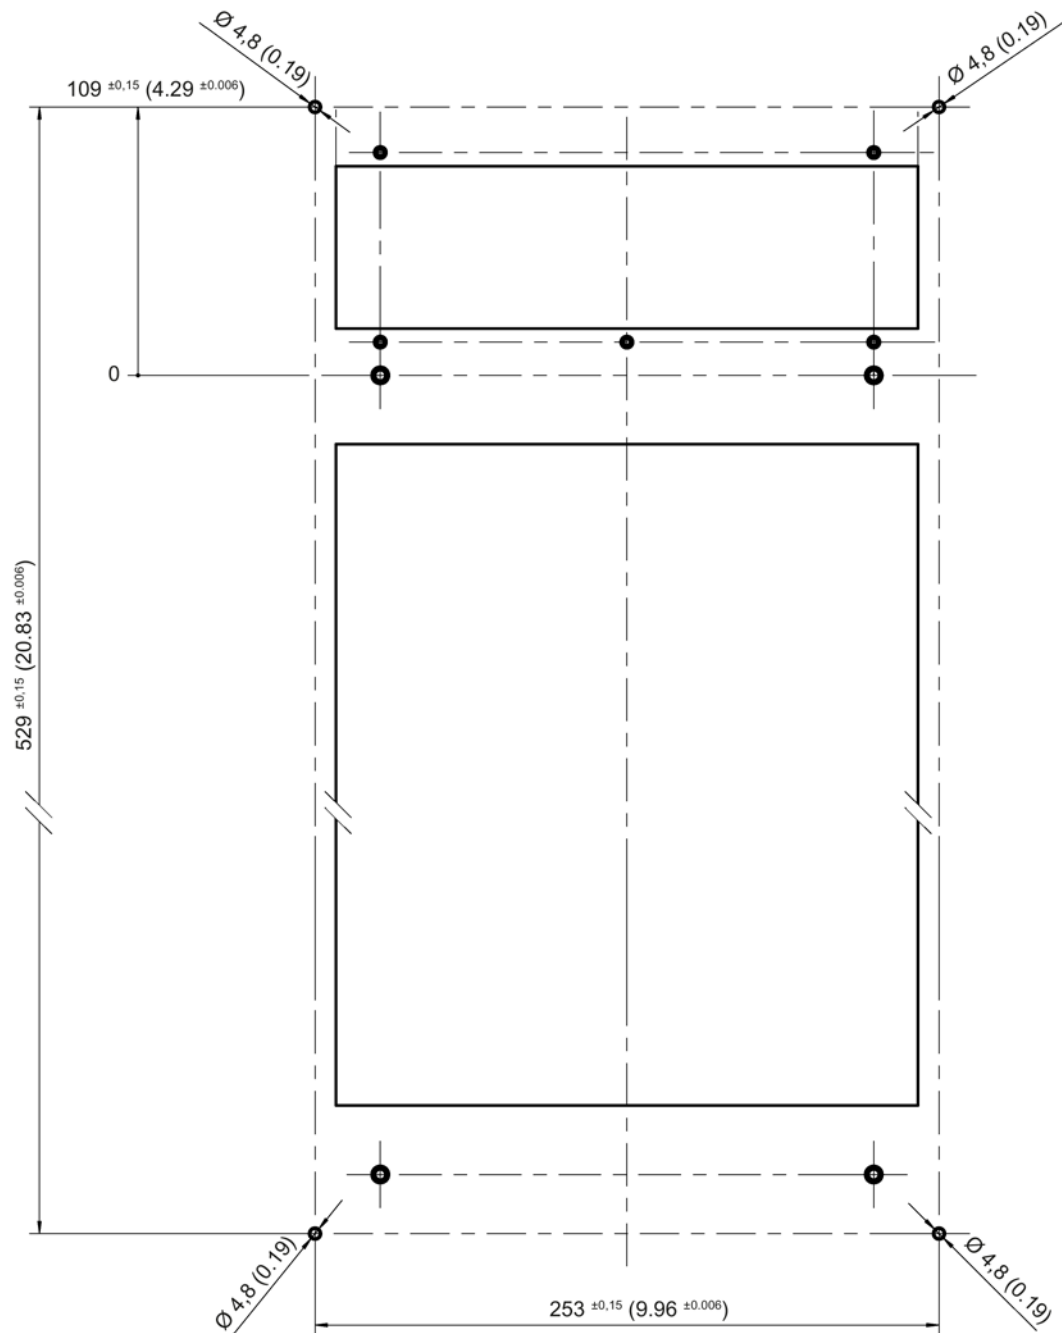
Bohrbild zur Montage der Versteifungsbleche
